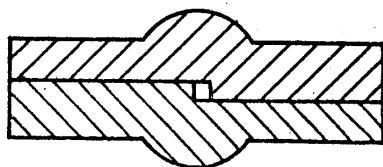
Контрольный образец – имитатор сварного соединения
